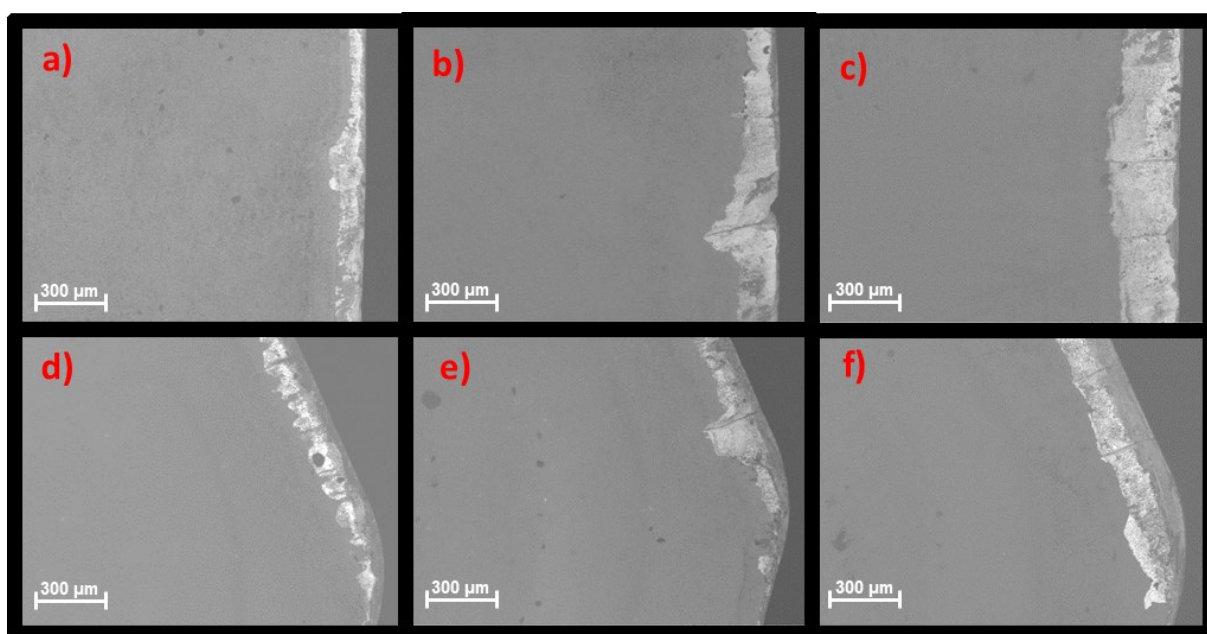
Fotos dos desgastes das ferramentas revestidas com TiAlN usadas na usinagem das placas com pré-furos a seco. a) Desgaste de flanco na usinagem do CGI A; b) Desgaste de flanco na usinagem do CGI B; c) Desgaste de flanco na usinagem do CGI C; d) desgaste de cratera, na usinagem do CGI A; e) desgaste de cratera, na usinagem do CGI B; f) desgaste de cratera, na usinagem do CGI C.
